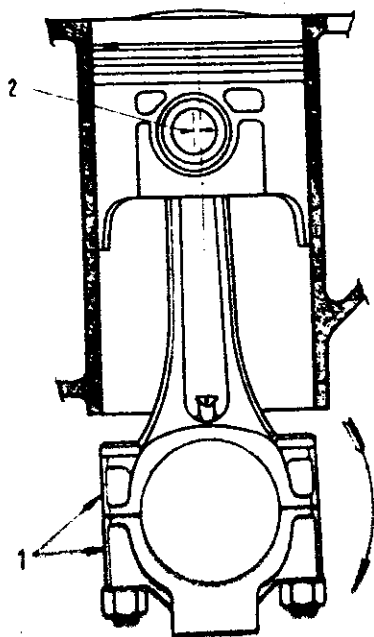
Montaje del conjunto pistón-biela en el cilindro.
